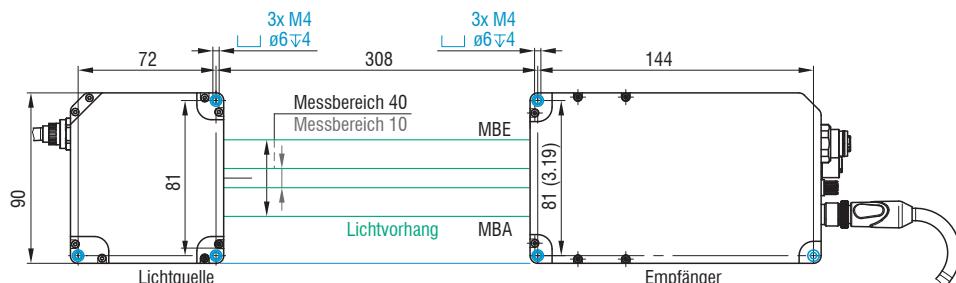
Montagegewinde für Direktverschraubung ODC2700-10, ODC2700-40, Abmessungen in mm
